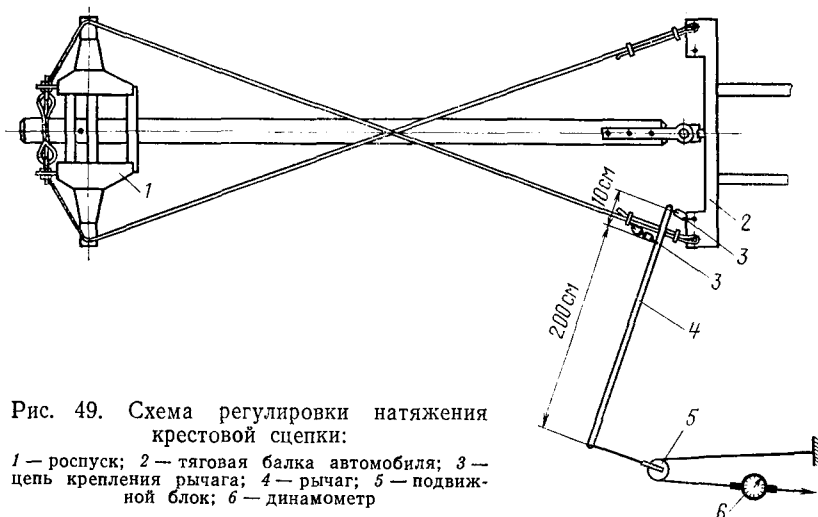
Схема регулировки натяжения крестовой сцепки:
